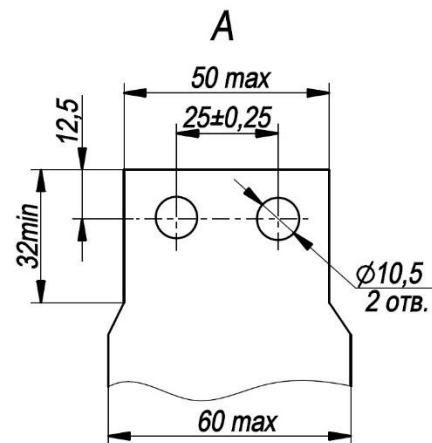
Присоединение от 1 до 4 жил кабеля (провода) без кабельного наконечника
